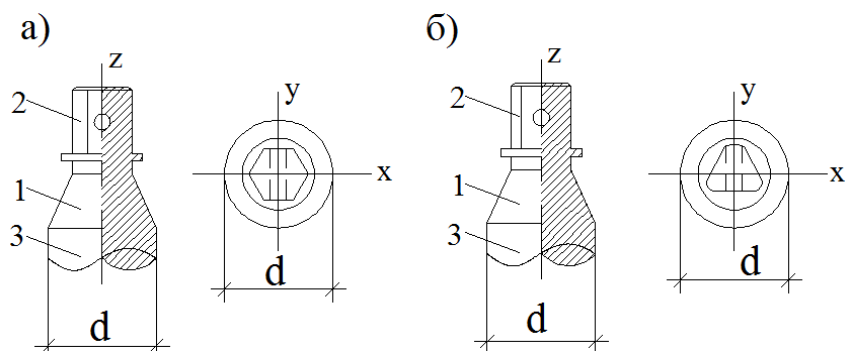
Типовые конструкции хвостовика РСу: а) шестигранного сечения;
